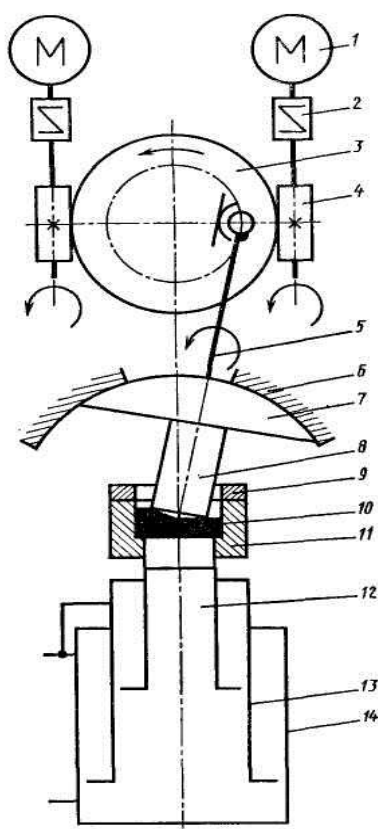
Кинематическая схема машины мод. РХW100А (ПНР) для осадки заготовок обкатыванием (Сферодвижной штамповкой)
